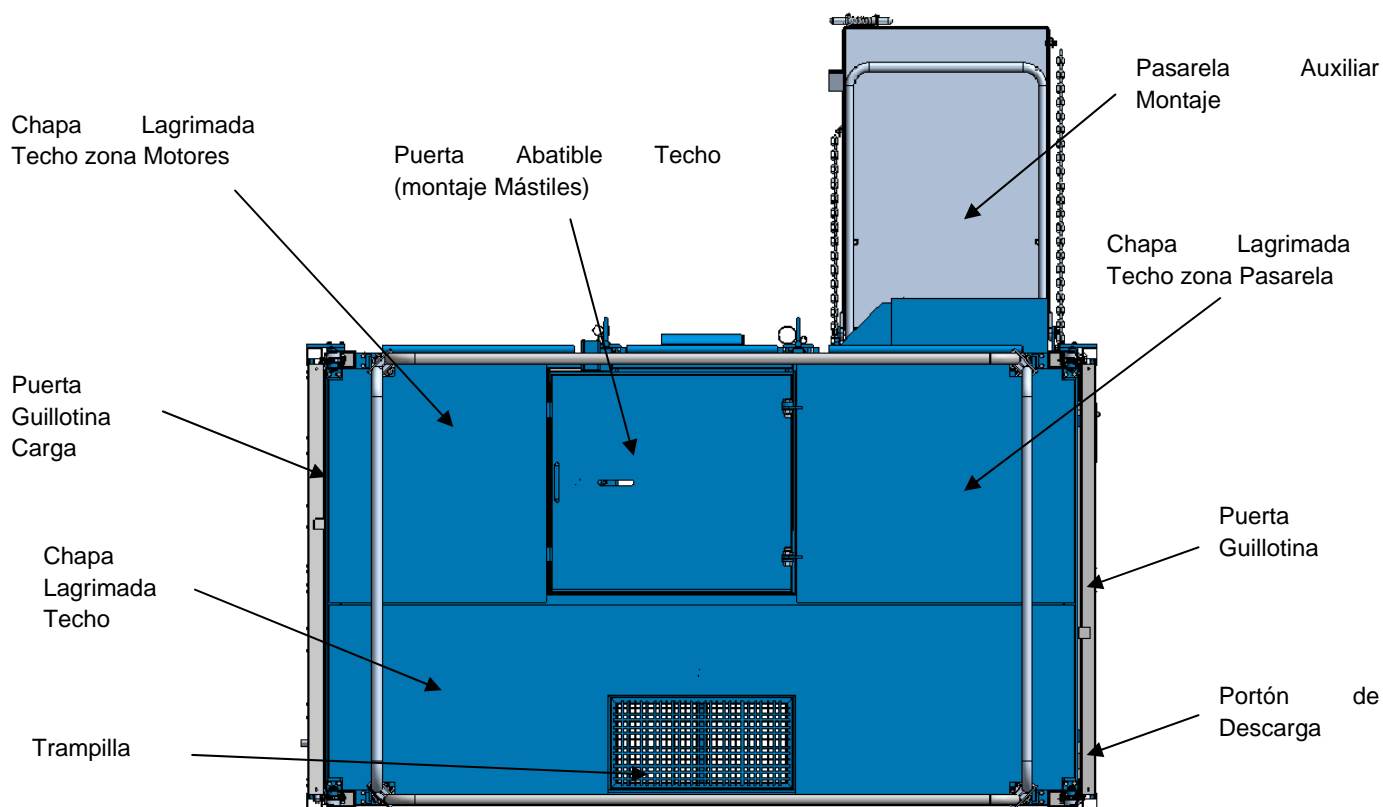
Cabina (Vista en planta, Puertas y Rampa Descarga abiertas)
